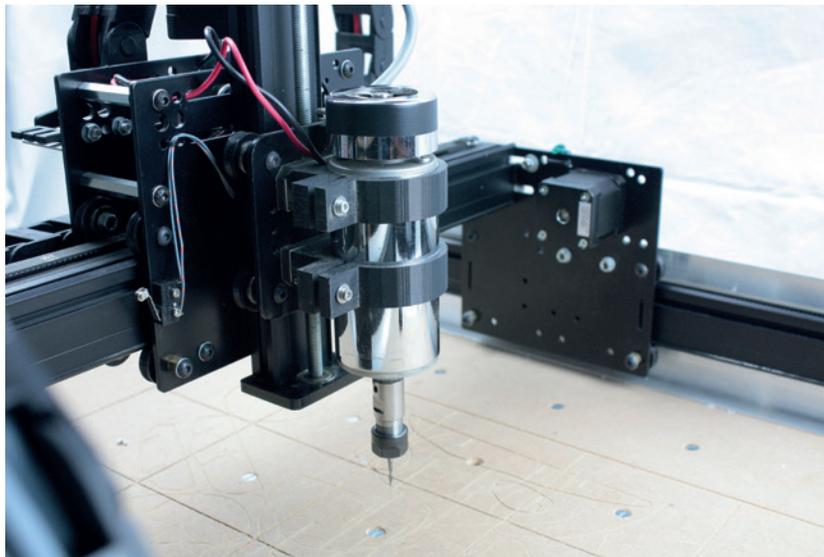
Zum Werkzeugwechsel fährt die Spindel an eine gut erreichbare Stelle.
